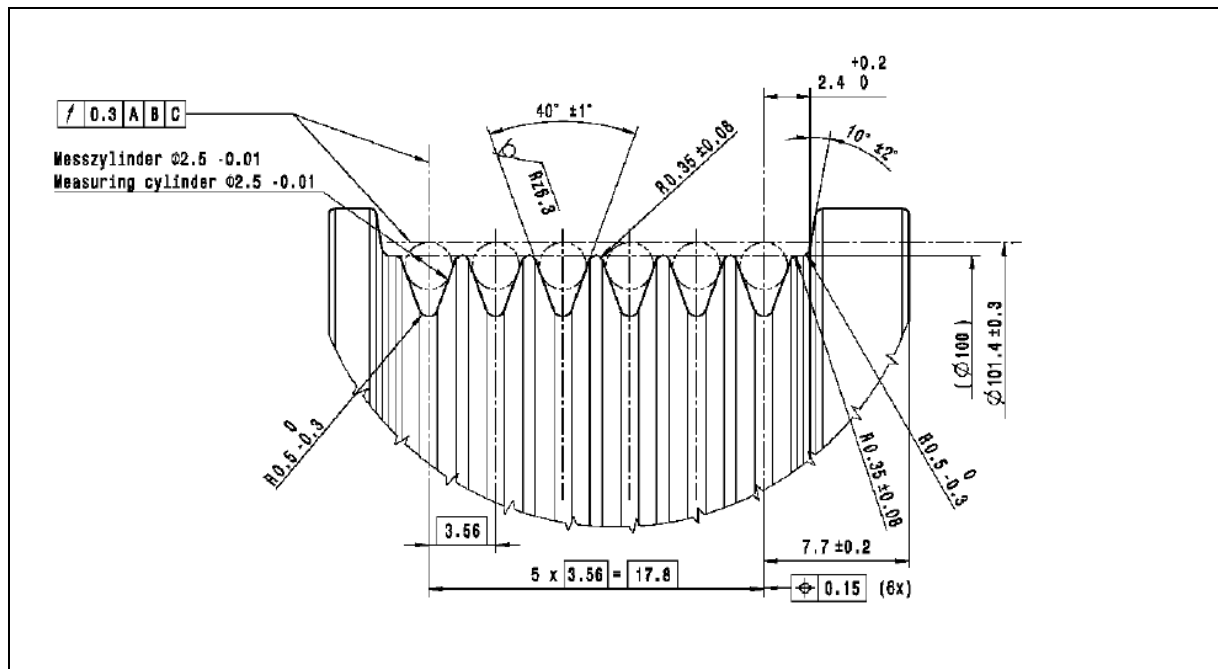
Детальное изображение U – Шкив компрессора климатической установки (пример: DENSO-7SEU17)
